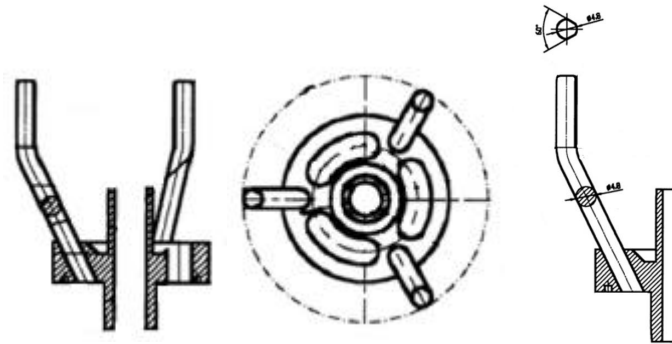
하단안내집합체(Bottom Guide Assembly) 부품도
